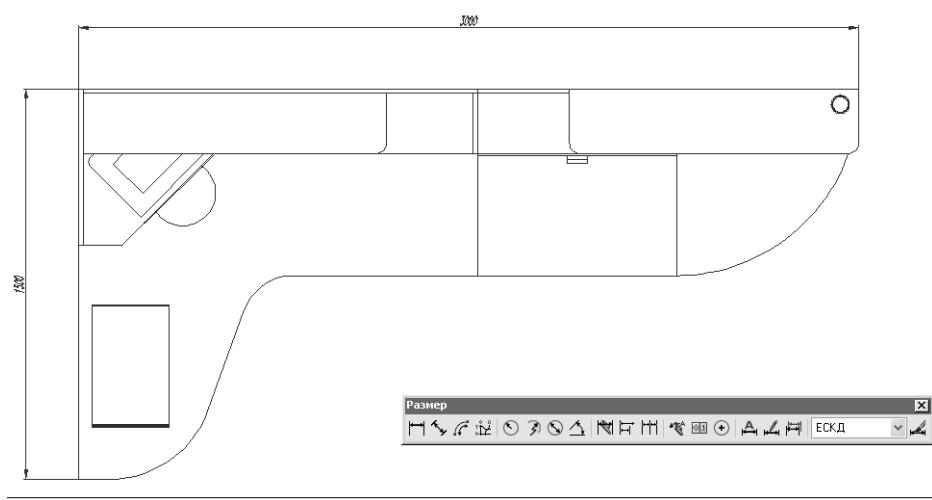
▼ Вертикальный и горизонтальный размеры
